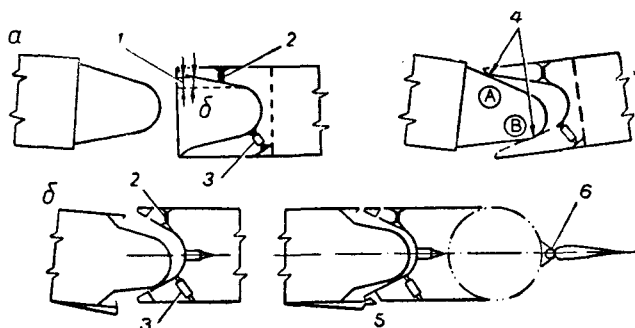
Схема стыковки с коническими направляющими: а — одинаковая конусность; б — различная конусность; 1 — допустимый промах; 2 — пружина; 3 — демпфер; 4 — высокое контактное напряжение; 5 — фиксатор; 6 — выравнивающий двигатель.
